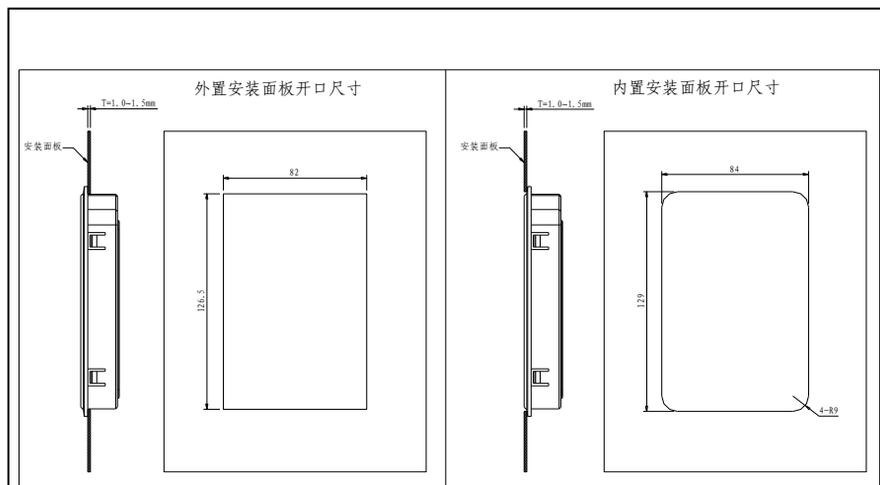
键盘安装开口尺寸图(尺寸单位: mm)
